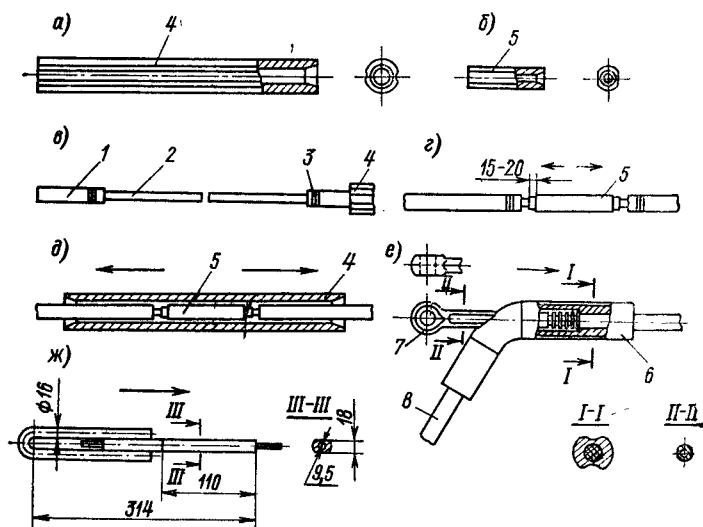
Прессуемые зажимы и их монтаж: а — алюминиевый корпус соединительного зажима; б — стальной сердечник соединительного зажима (соединительный зажим для стального каната); в — д — последовательность монтажа соединительного зажима; е — натяжной зажим типа НАС; ж — зажим типа НС-50-1 для стальных канатов сечением 50 мм²
